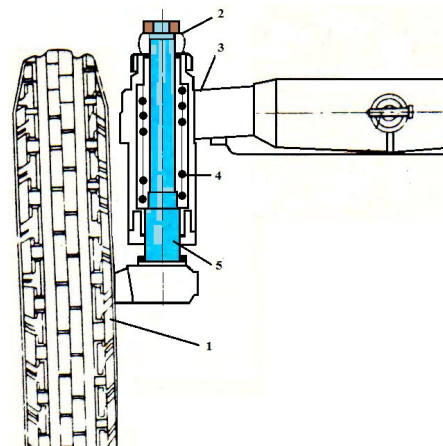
Схема подвески трактора с индивидуальным подрессориванием колеса:
